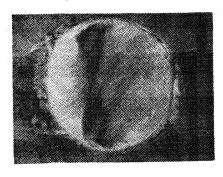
Срез доброкачественной сварной точки после испытания
